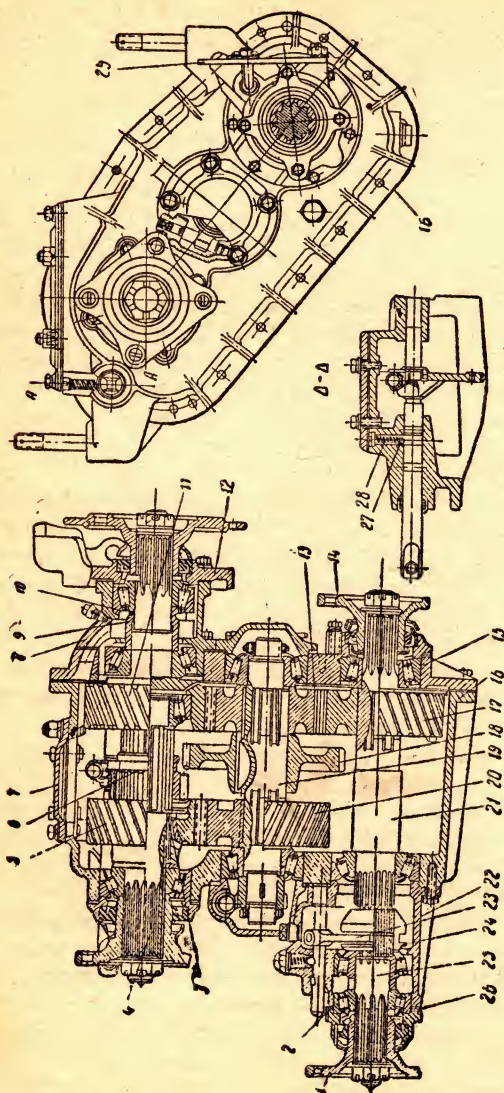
Раздаточная коробка автомобиля ЗИЛ-157К:
